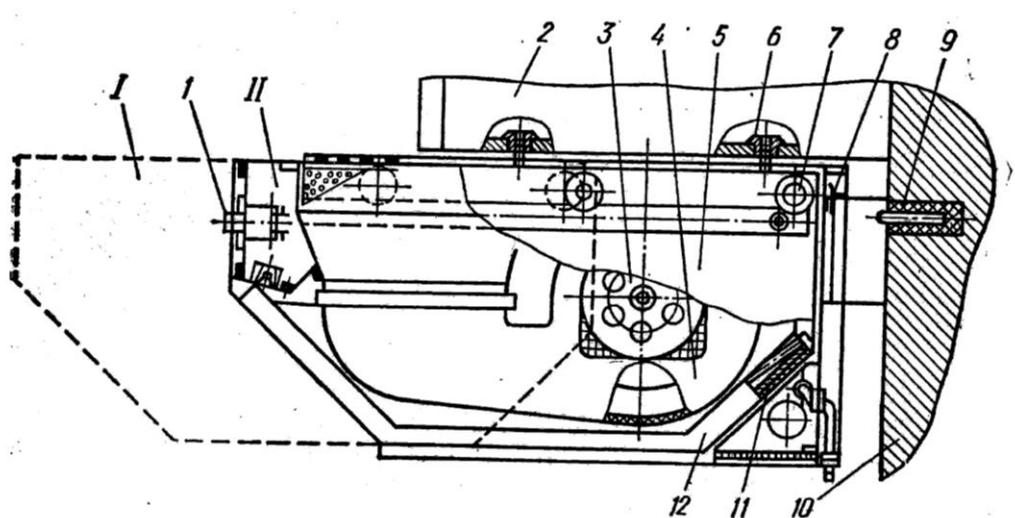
Электрофильтр ВБ-3 «Славитуч»: 1 - выключатель; 2 - кухонный шкаф; 3 – электродвигатель; 4 - вентилятор; 5 - каретка; 6 - болты; 7 - ролики; 8 – пазы отверстия; 9 - винты; 10 - стена; 11 – фильтрующий материал ; 12 - боковая рамка
